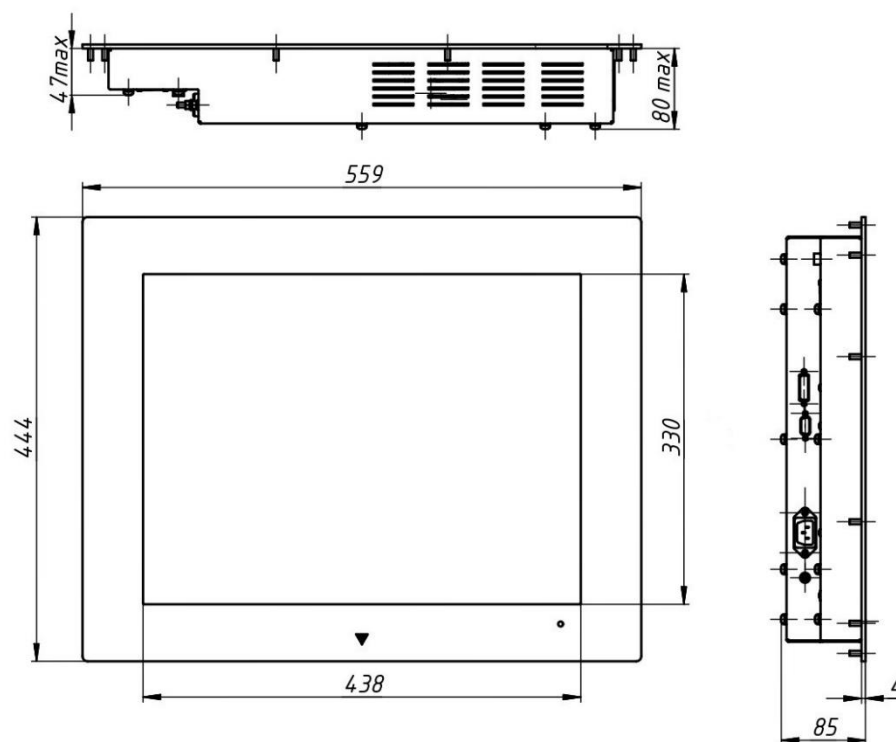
Габаритный чертёж видеомонитора в исполнении ВМП1225-АД-8-Х-Х-Х.
